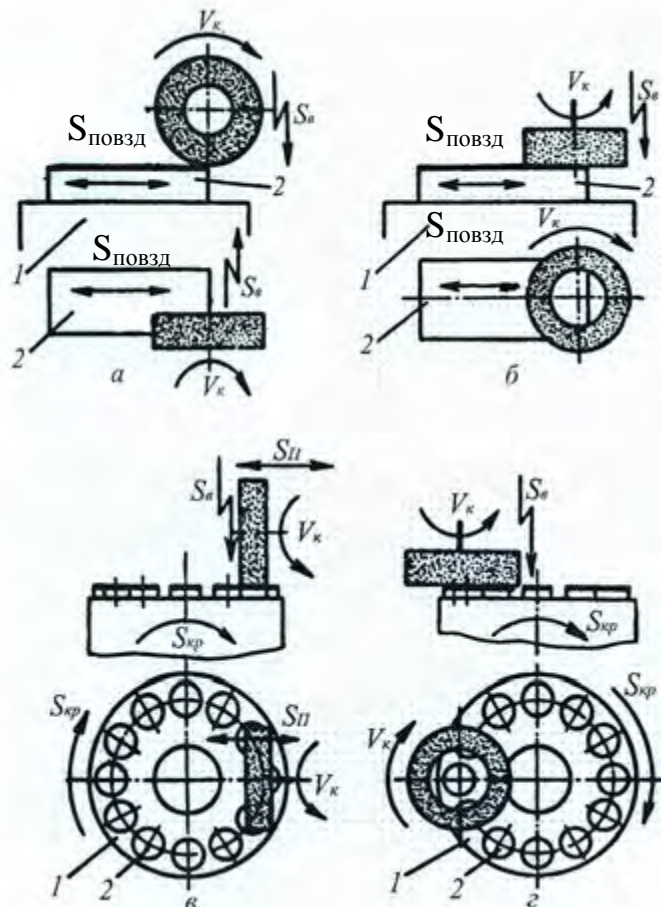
Схеми оброблення заготовок на плоскошліфувальних верстатах
